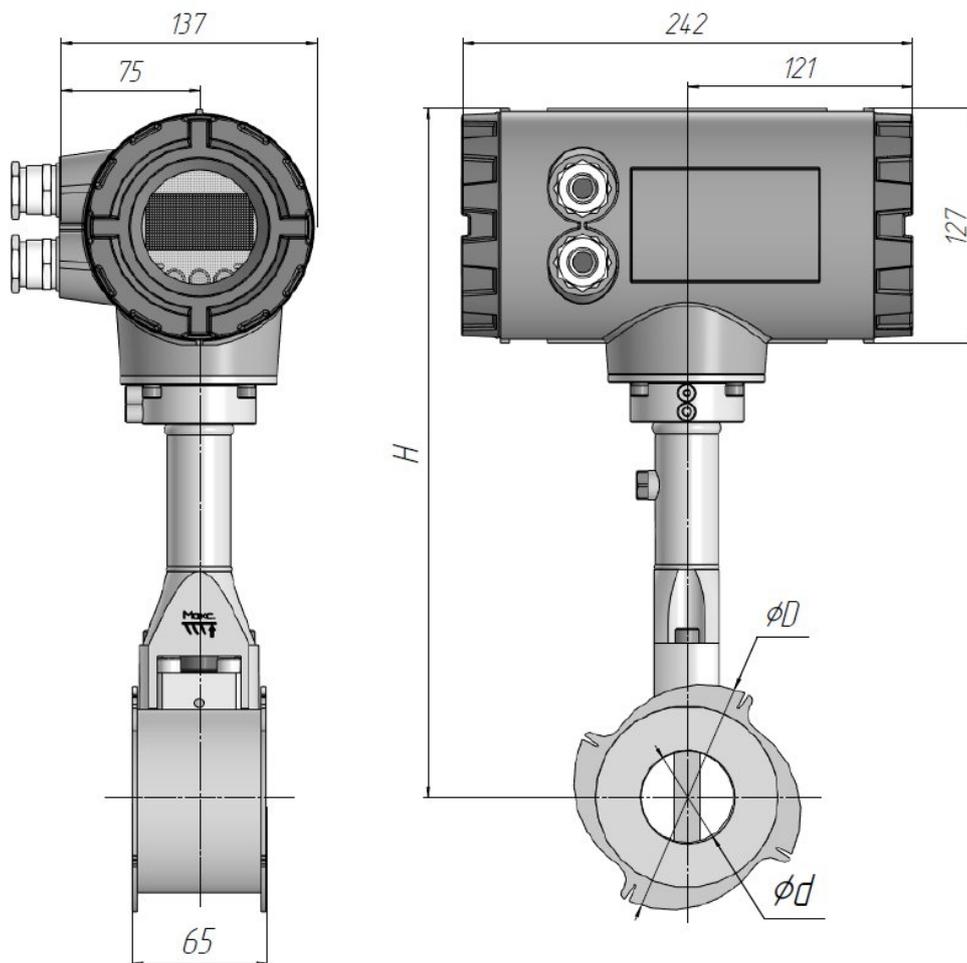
Габаритные размеры расходомера с бесфланцевым типом присоединения («сэндвич»)
